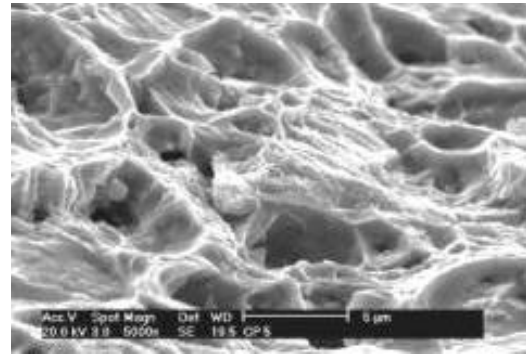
Fractografia por MEV da junta soldada com o consumível ERNiCr-3.
